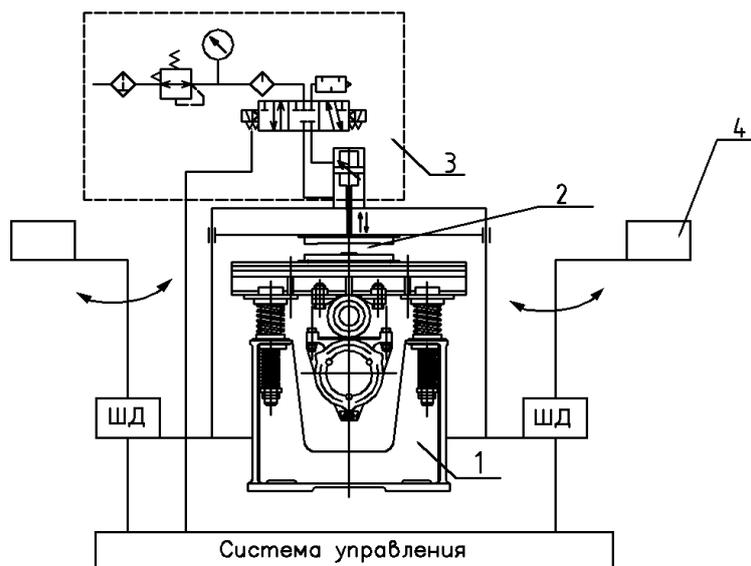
Структурная схема установки для правки фрикционных дисков: 1) вибростенд; 2) рабочая зона; 3) пневмосистема; 4) загрузочно-разгрузочный механизм
